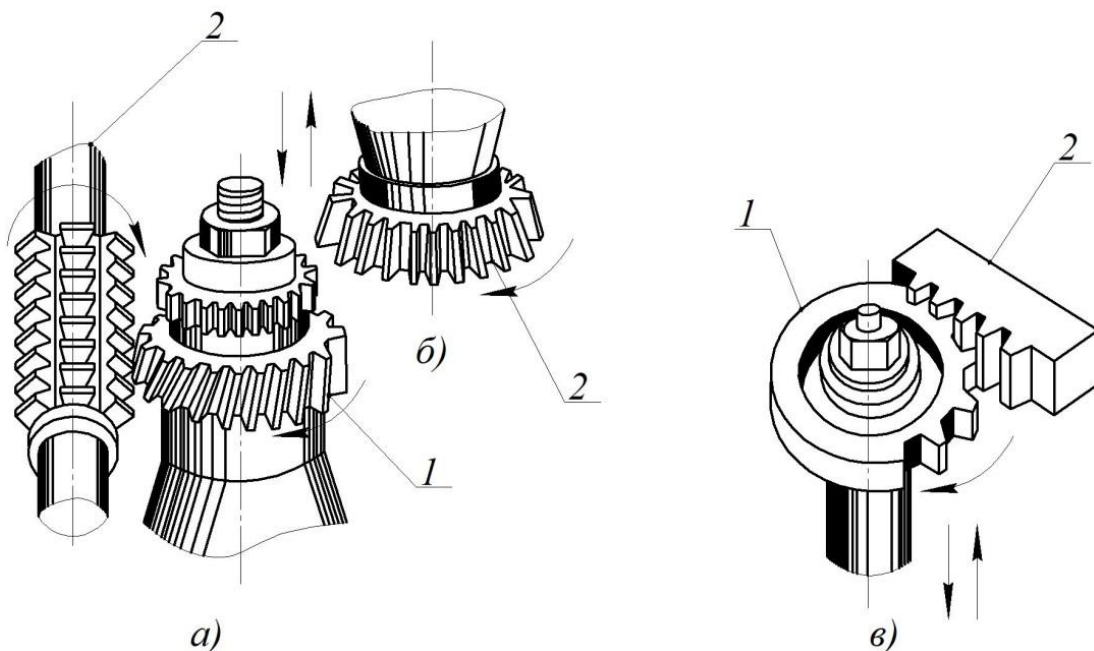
Схеми нарізування циліндричних зубчастих коліс методом обкатування: *a* – черв'ячною фрезею; *б* – дисковим довб'яком; *в* – гребінкою;
